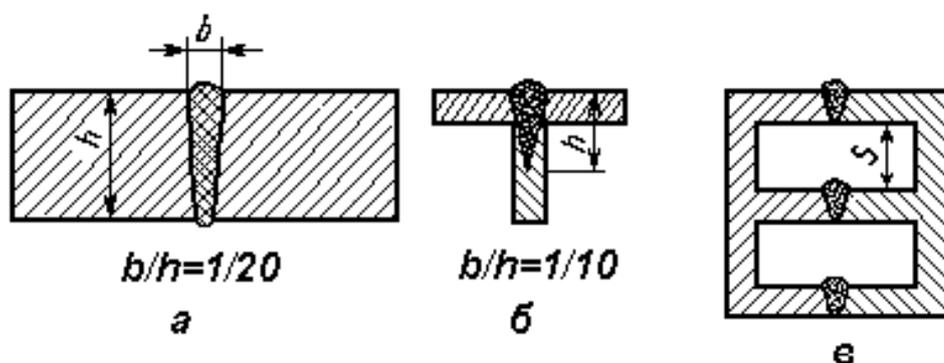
Типы сварных соединений, выполняемых электронно-лучевой сваркой
